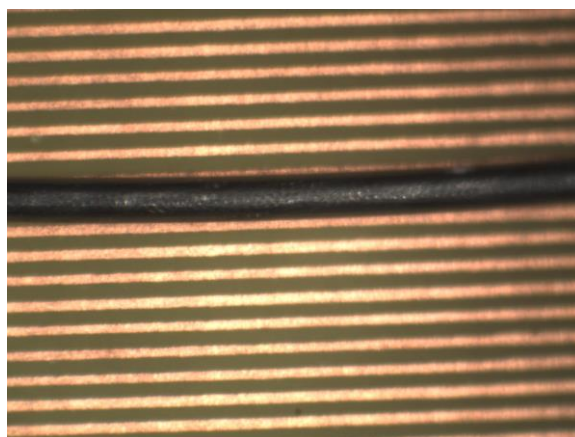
Detalle del PCB con un cable de 360 μm de diámetro
